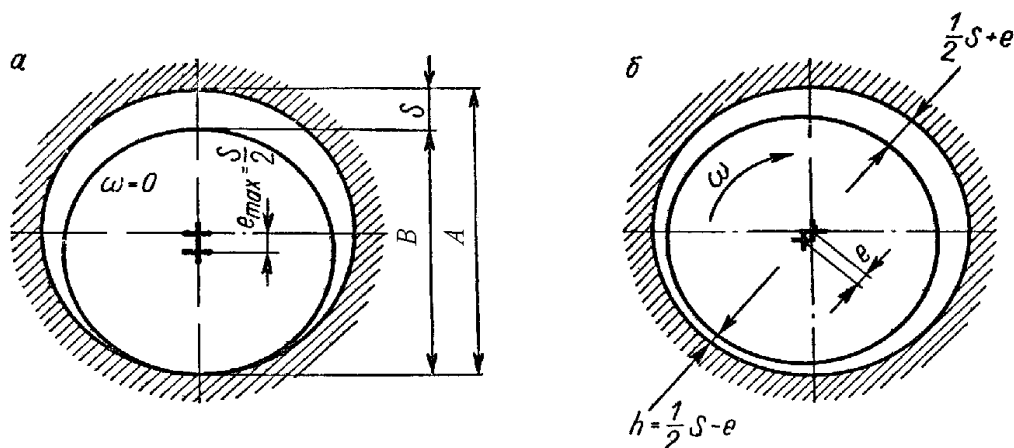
Схема сопряжения: *a* – вал неподвижен; *б* – вал вращается; A – размер отверстия; B – размер вала; S – зазор; h – масляный слой
